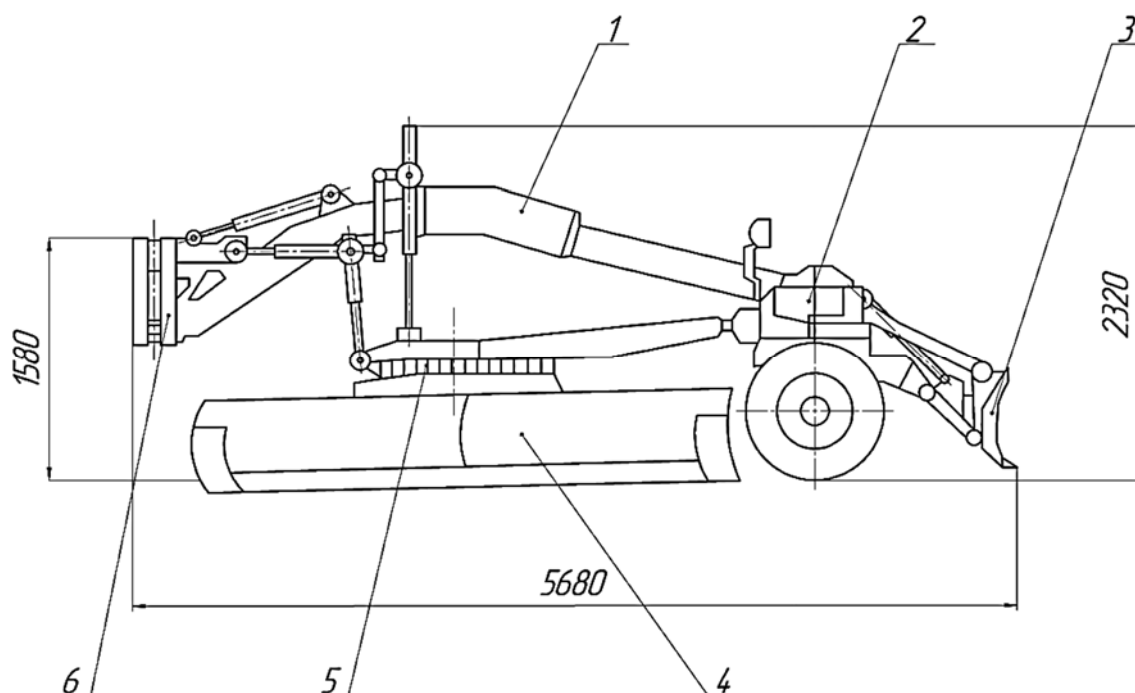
Общий вид полуприцепного грейдера с передней навеской: 1 – рама; 2 – поворотный узел; 3 – бульдозерный отвал; 4 – грейдерный отвал; 5 – поворотный круг; 6 – шарнир поворота рамы
